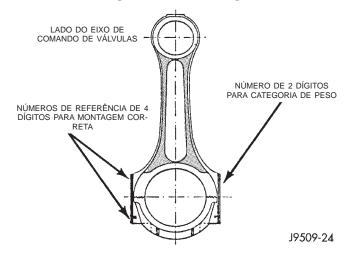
Identificação da Biela INSPEÇÃO — PINO DO PISTÃO
